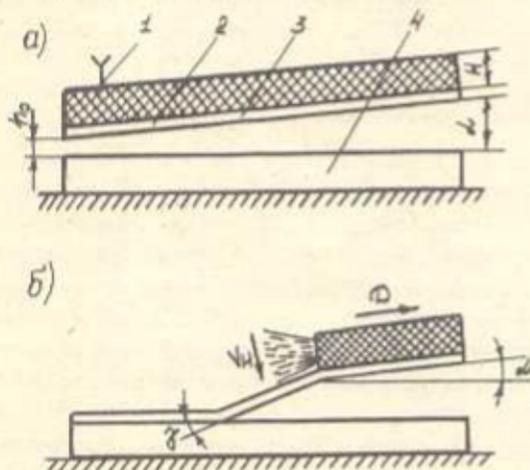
Принципиальная схема сварки взрывом: а) перед сваркой; б) во время сварки
